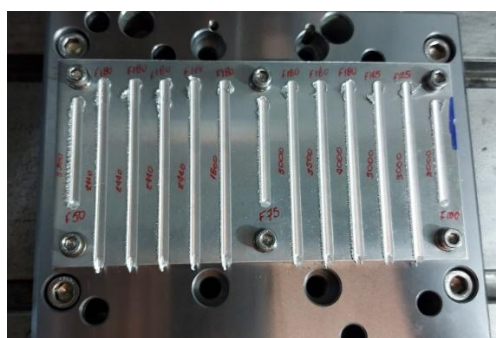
Fixação do material a processar no centro de usinagem CNC.
